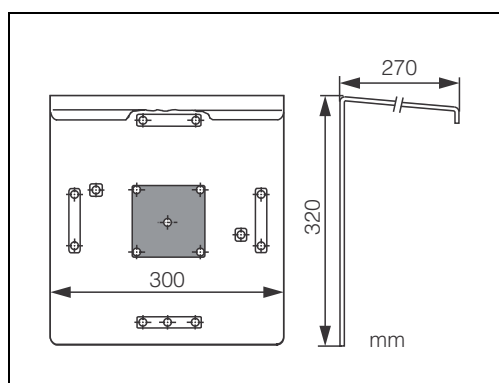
Tettuccio di protezione dalle intemperie CYY101
